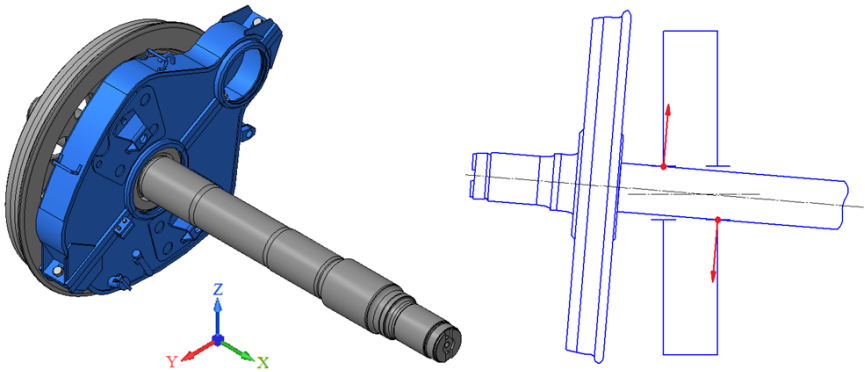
Условная схема нагружения кожуха зубчатой передачи при вписывании тележки в кривую
